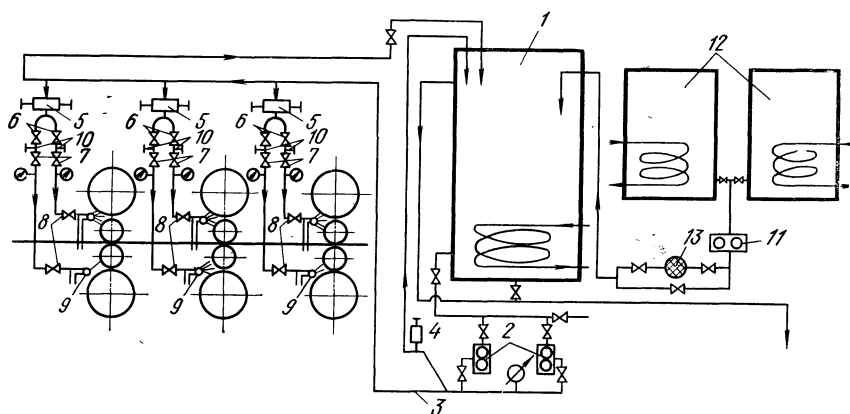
Схема установки для подачи технологической смазки в коллектор охлаждающей воды на НТЛС 1680 (завод «Запорожсталь»)
